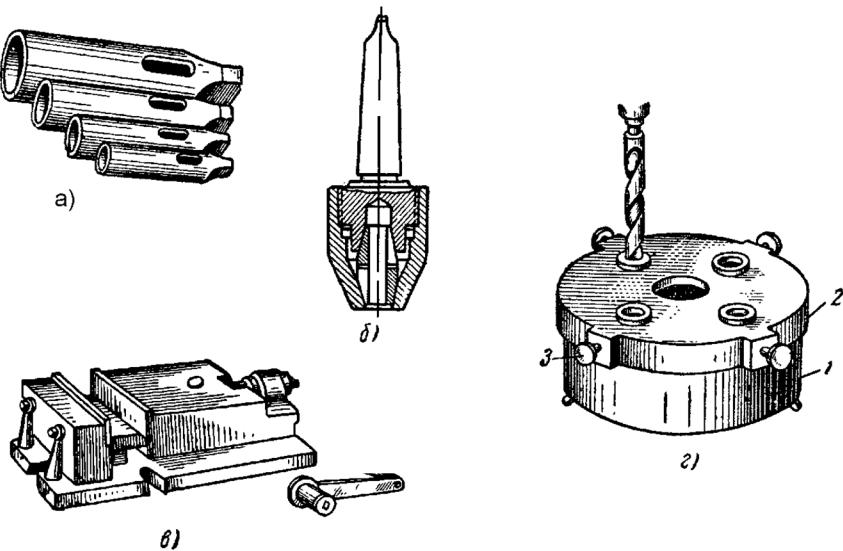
Принадлежности и приспособления к сверлильным станкам:
